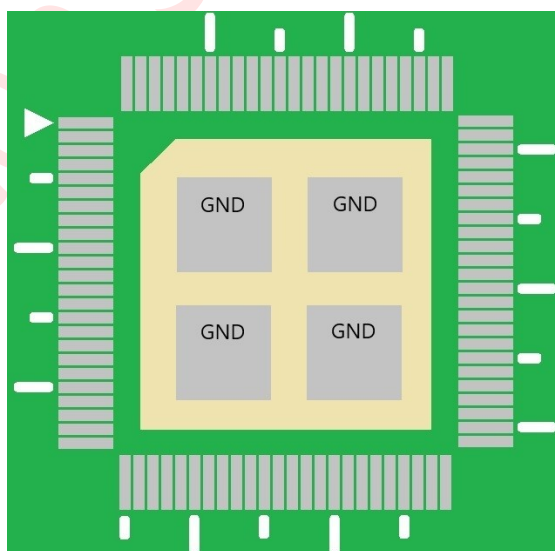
：LT779C 底部焊盘 PCB 的设计建议-2
